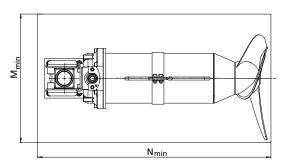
Установка принадлежностей 22 - Атматіх 400 (только типоразмер 4135) / 600
